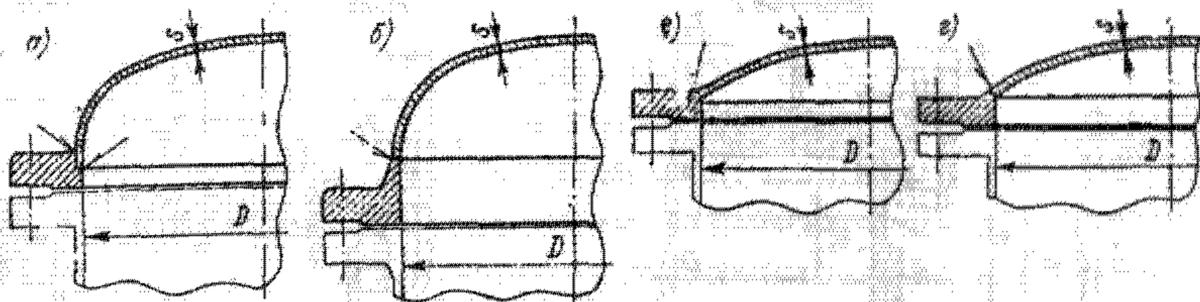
Типовые конструкции отъемных выпуклых крышек в стальных сварных аппаратах: а — эллиптическая с плоским фланцем; б — эллиптическая с фланцем, приварным встык; в — сферическая с угловым сварным соединением с фланцем; г — сферическая со стыковым сварным соединением с фланцем
